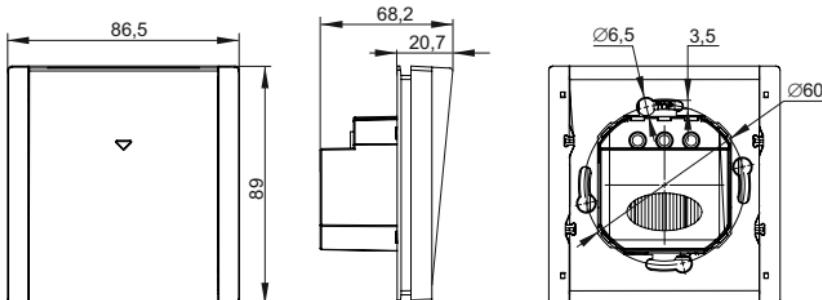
Габаритные и установочные размеры выключателя / Figure 1 – Overall and installation dimensions of the switch / 1 сурет – Ажыратқыштың габариттік және орнату өлшемдері / Figura 1 - Dimensiunile generale și de instalare ale întrerupătorului / Зураг 1 - Унтраалың овор ба суурилуулак хэмжээ / 1-rasm - Viklyuchatelning gabarlitlari bo'yicha va o'rnatilish natijasidagi o'lchamlari
